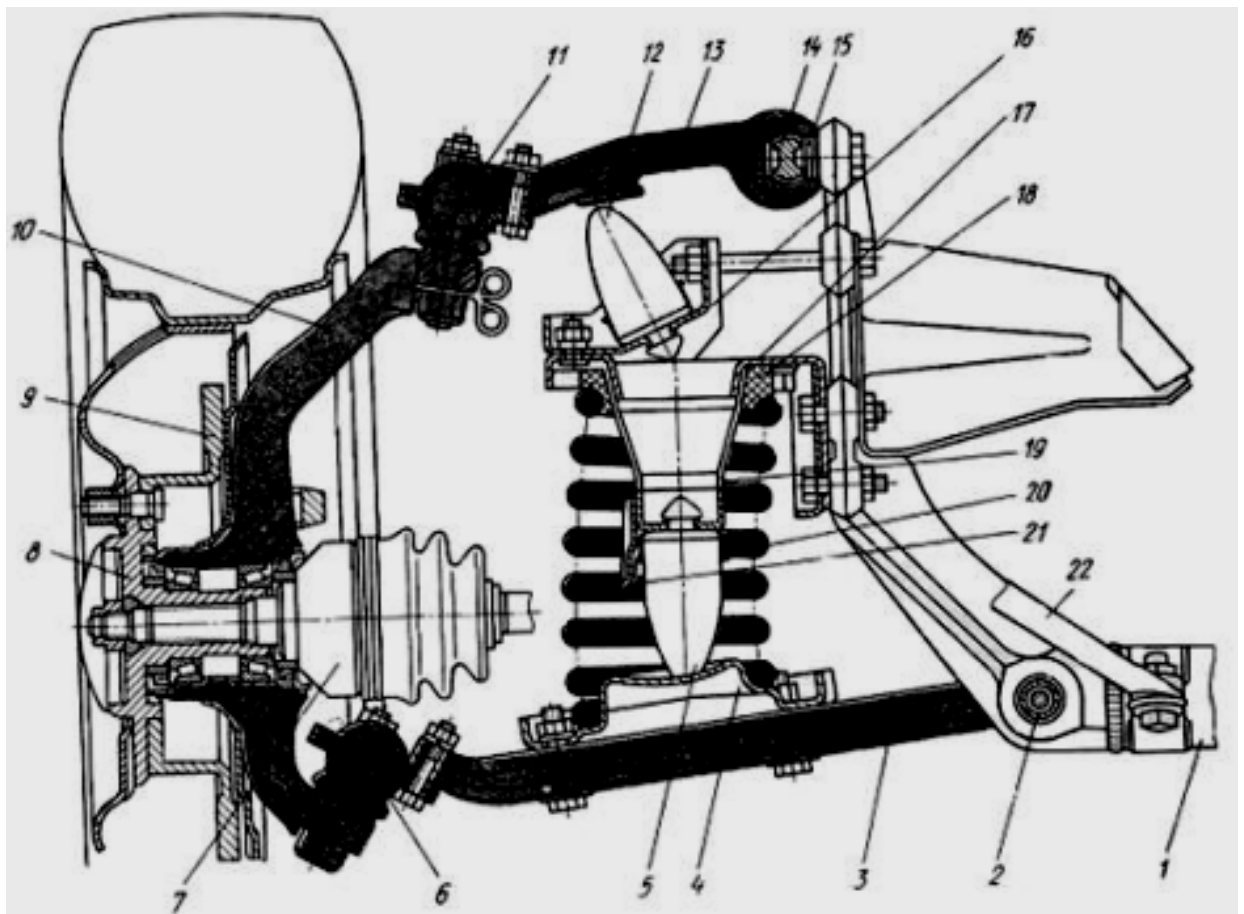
Передняя подвеска легкового автомобиля ВАЗ-2121 "Нива": 1 - поперечина; 2 - ось нижнего рычага; 3 - нижний рычаг; 4 и 17 соответственно нижняя и верхняя опорные чашки пружины; 5 - буфер сжатия; 6 и 11 - соответственно нижний и верхний шаровые шарниры; 7 - наружный шарнир привода переднего колеса; 8 - ступица; 9 - тормозной диск; 10 - поворотный кулак; 12 - буфер отдачи; 13 - верхний рычаг; 14 - ось верхнего рычага; 15 - регулировочные прокладки; 16 - кронштейн; 18 - виброшумоизолирующая прокладка; 19 - опора; 20 - пружина 21 - упор; 22 - растяжка
